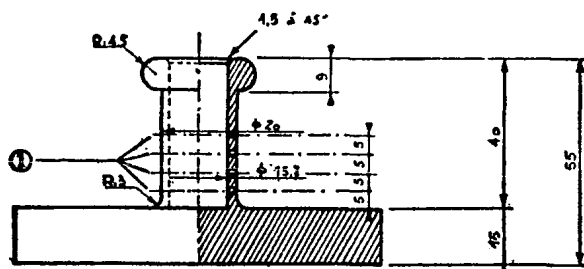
Cylindre creux en bronze, fermé d'un côté; plan et coupe verticale
